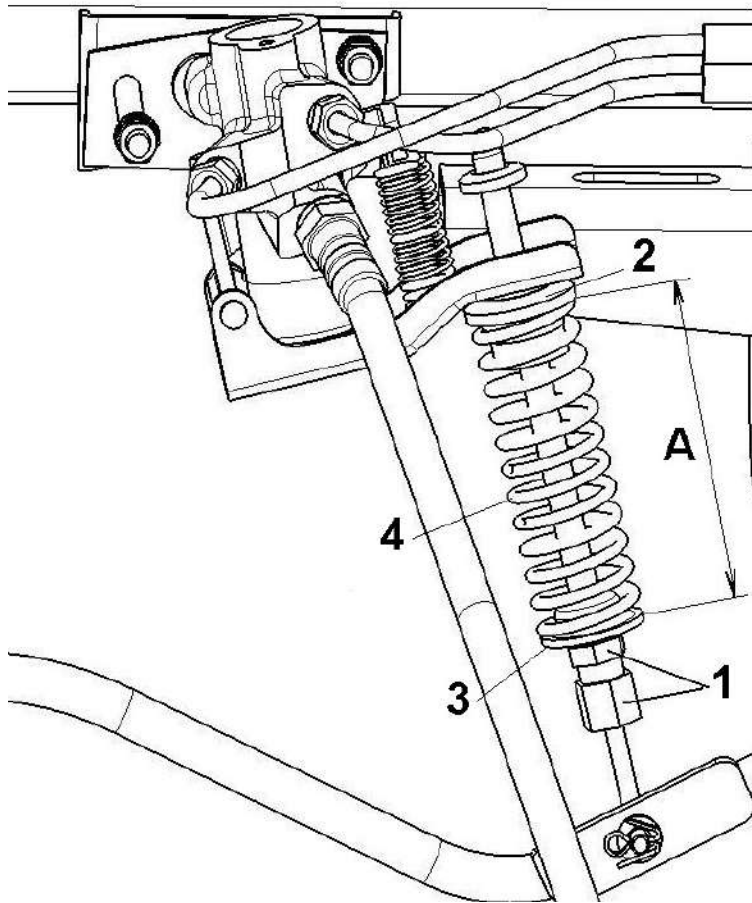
Схема регулировки привода регулятора давления: 1- цанговый зажим тяги привода регулятора; 2 и 3 – упорные шайбы; 4- пружина; А- регулировочный размер
